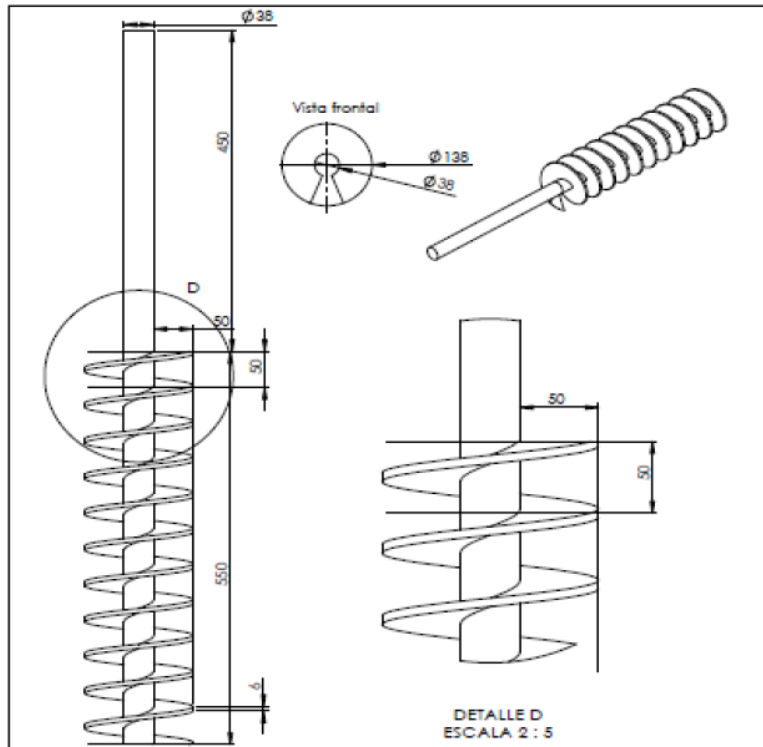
Dimensiones del tornillo extrusor, con las medidas de mm. Fuente: (Arroyo, 2016)
